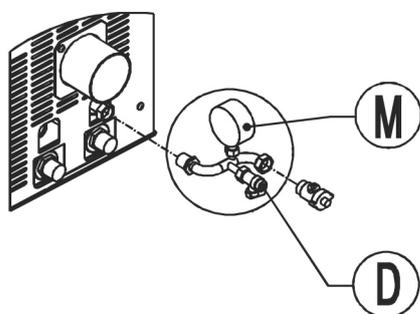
Terminale con rubinetto di caricamento (D) e manometro (M)
